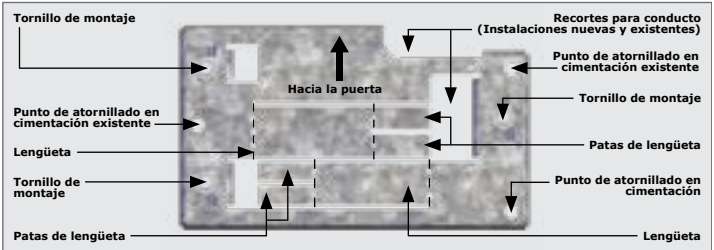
ENSAMBLE DE LA PLACA BASE
